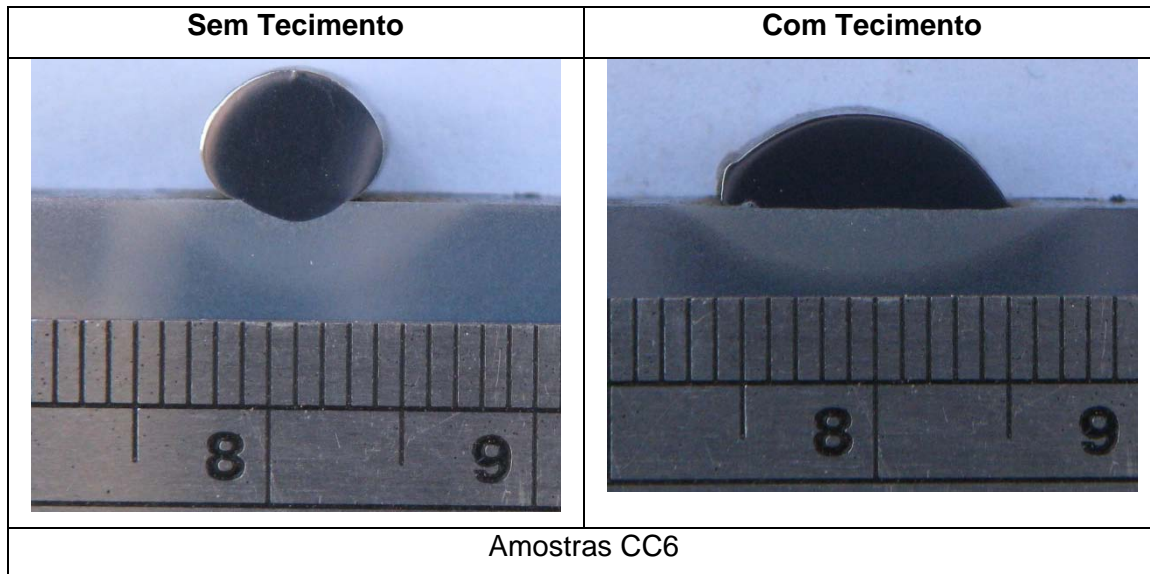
Seção transversal das amostras soldadas na condição CC6 com DPEP de 14 mm.
